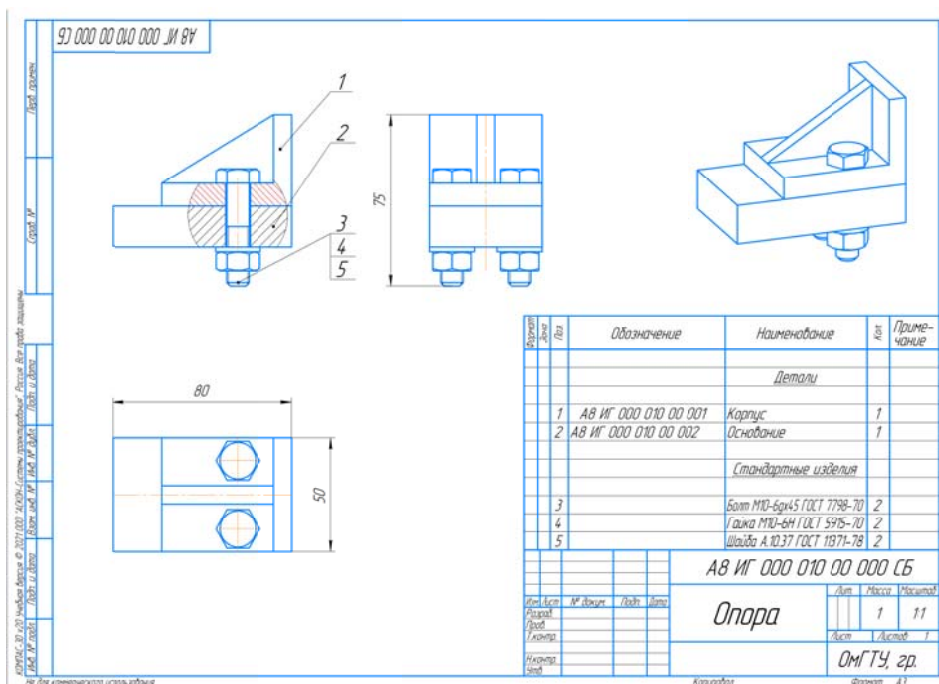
Готовый сборочный чертеж совместно со спецификацией
